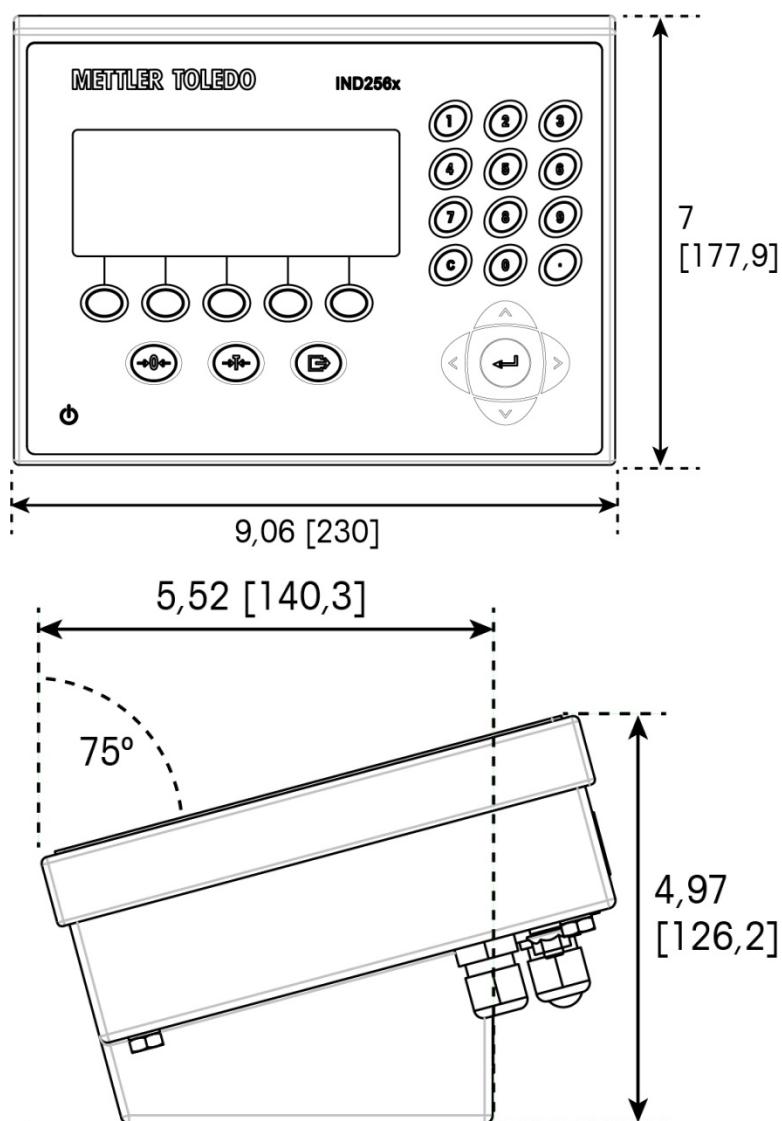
Dimensions de l'IND256x, installation de bureau
